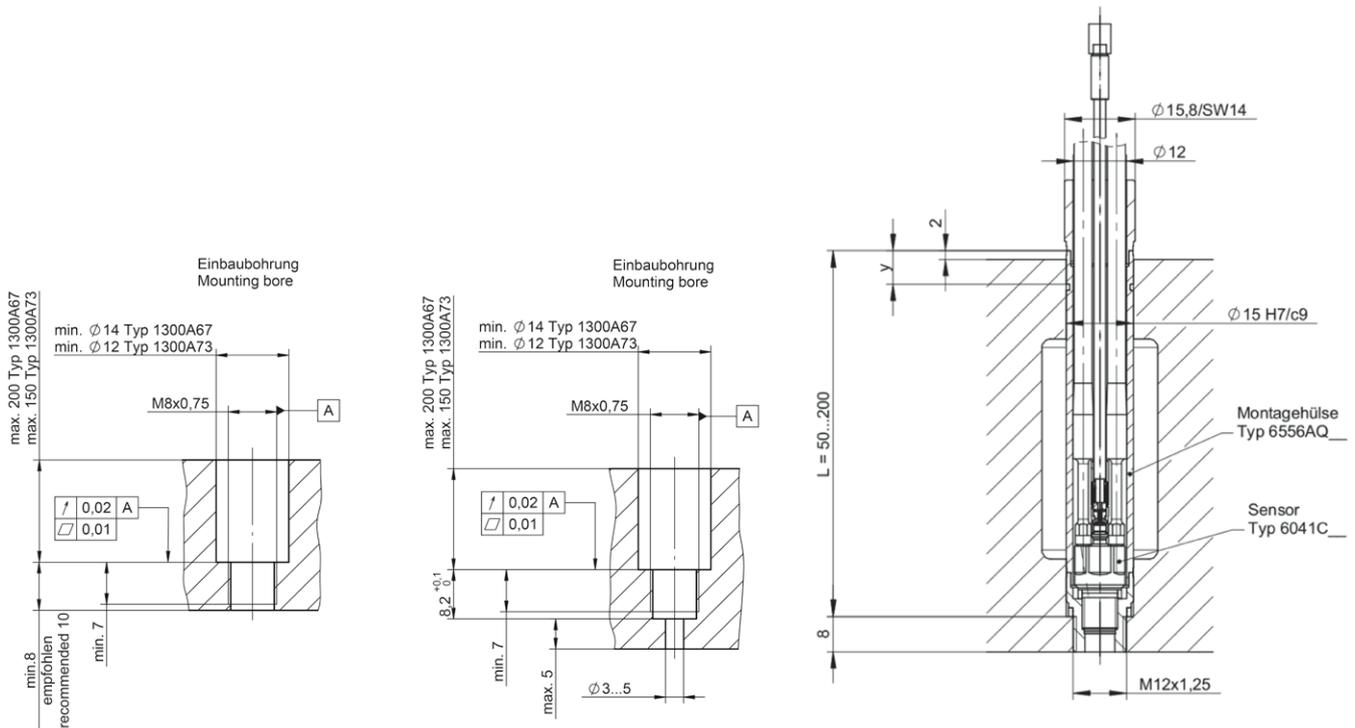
Brentraumbündige Einbaubohrung Abb. 2: Zurückversetzte Einbaubohrung Abb. 3: Sensoreinbau mit Montagehülse
